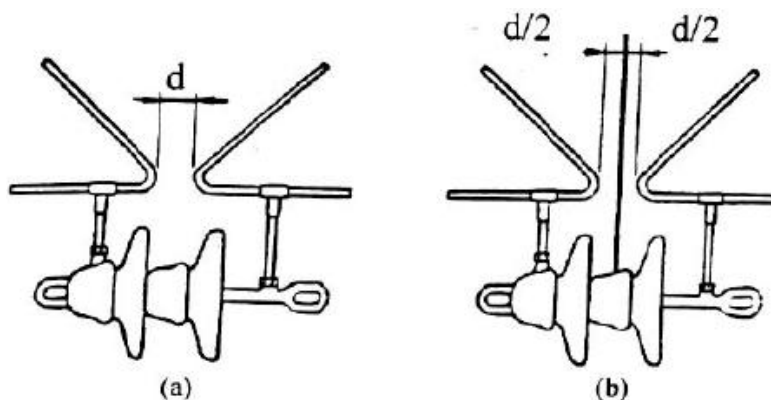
Detalhes Construtivos dos Centelhadores Tipo “chifre”
